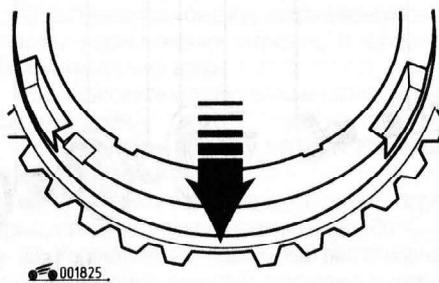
Отсутствующий зуб на кольце синхронизатора I передачи
